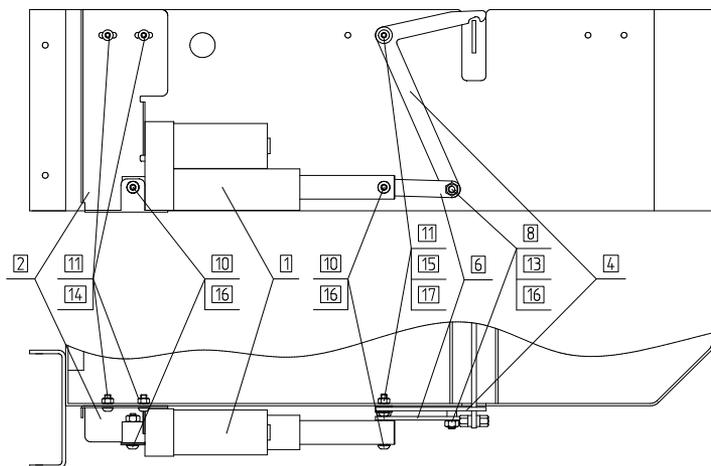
Установка привода с рычагами на ОУ Каскад типа
